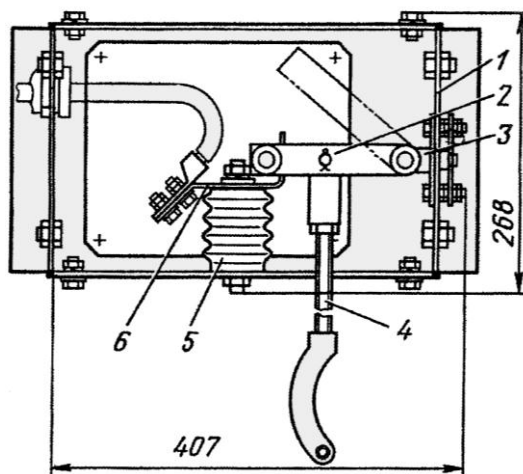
Разъединитель высоковольтный однополюсный РВО-010
